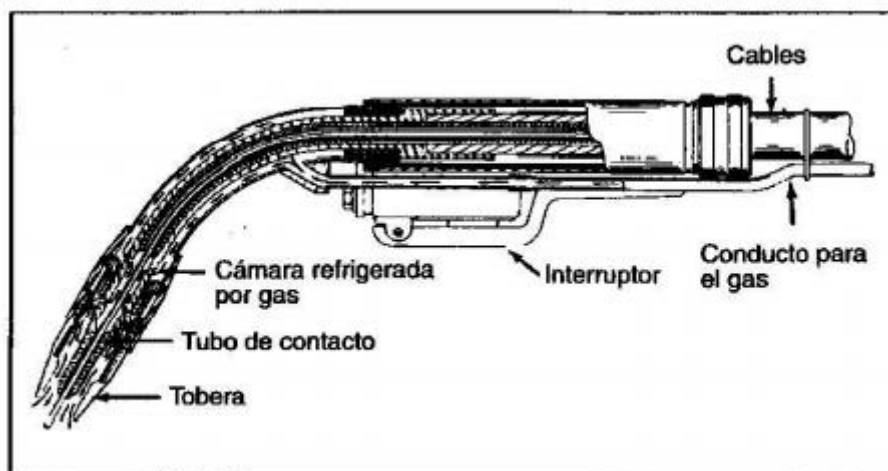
(B): PISTOLAS PARA EL SOLDEO CON PROTECCIÓN DE GAS
